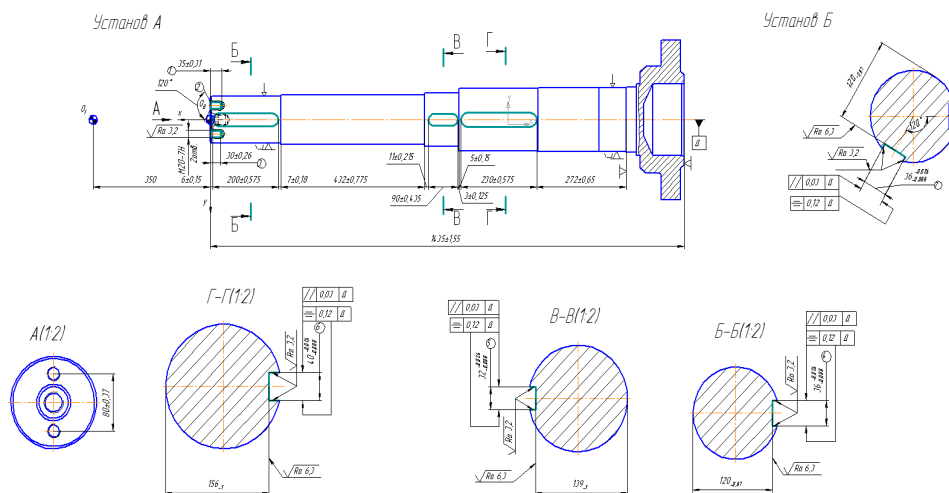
Ескіз механічної обробки деталі вал зубчастий
